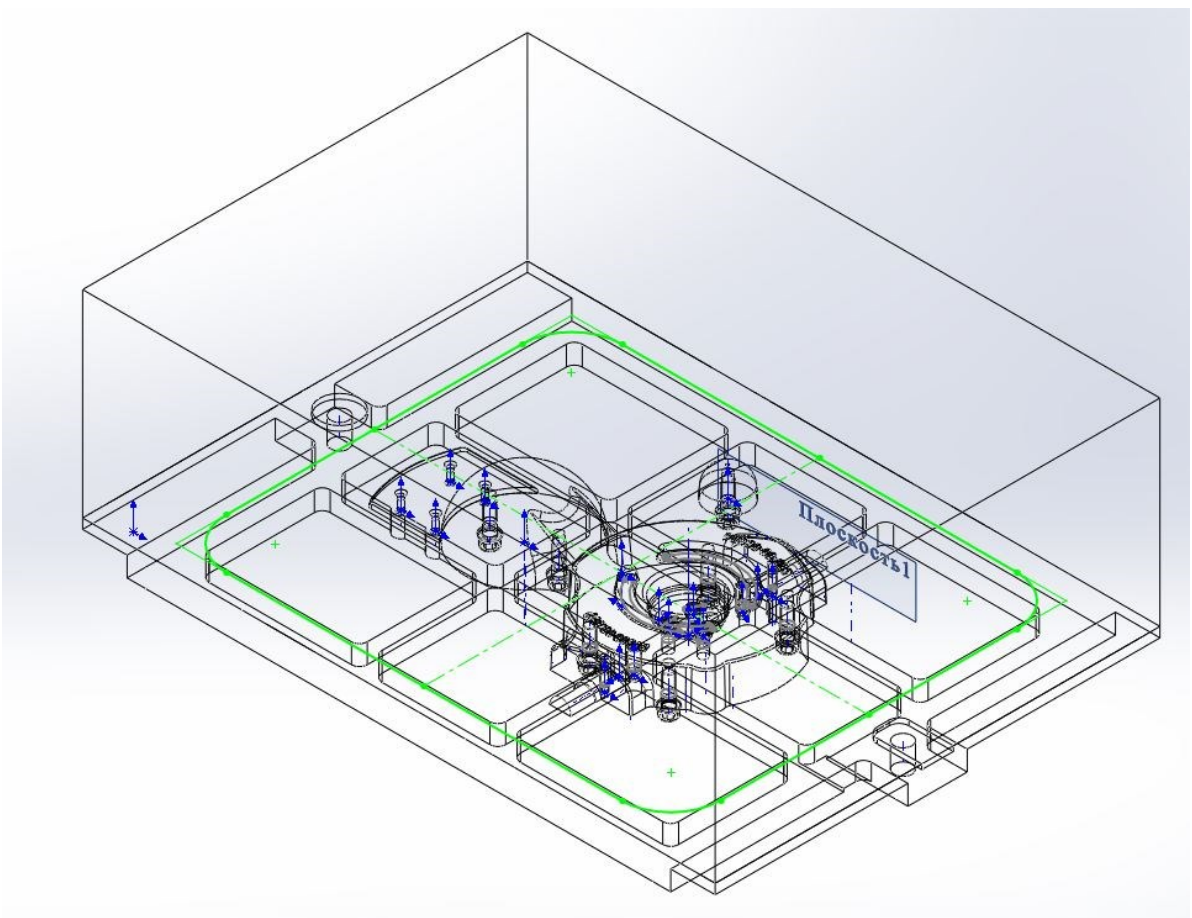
Проміжна 3Д зборка для створення порожнини
